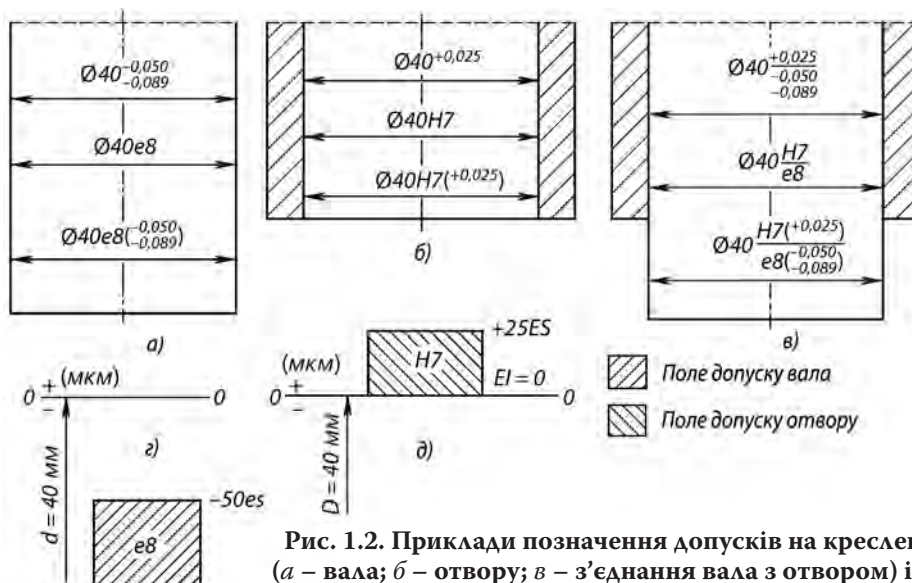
Приклади позначення допусків на кресленниках (а – вала; б – отвору; в – з'єднання вала з отвором) і схеми розташування полів допусків (г – вала; д – отвору)
